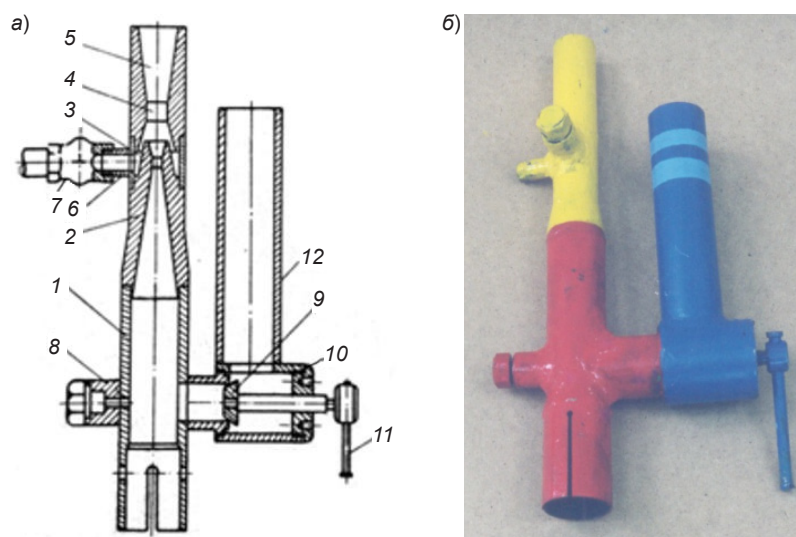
Схема (а) и опытный образец (б) эжекторного напорно-вакуумного устройства: 1 — корпус; 2 — коническое сопло; 3 — приемная камера; 4 — смешительная камера; 5 — диффузор; 6 — патрубок; 7 — задвижка для соединения эжектора к магистрали очистителя; 9 — клапан; 10 — винт; 11 — ручка для регулировки давления выхлопного газа перед соплом; 12 — газоотводящий патрубок
